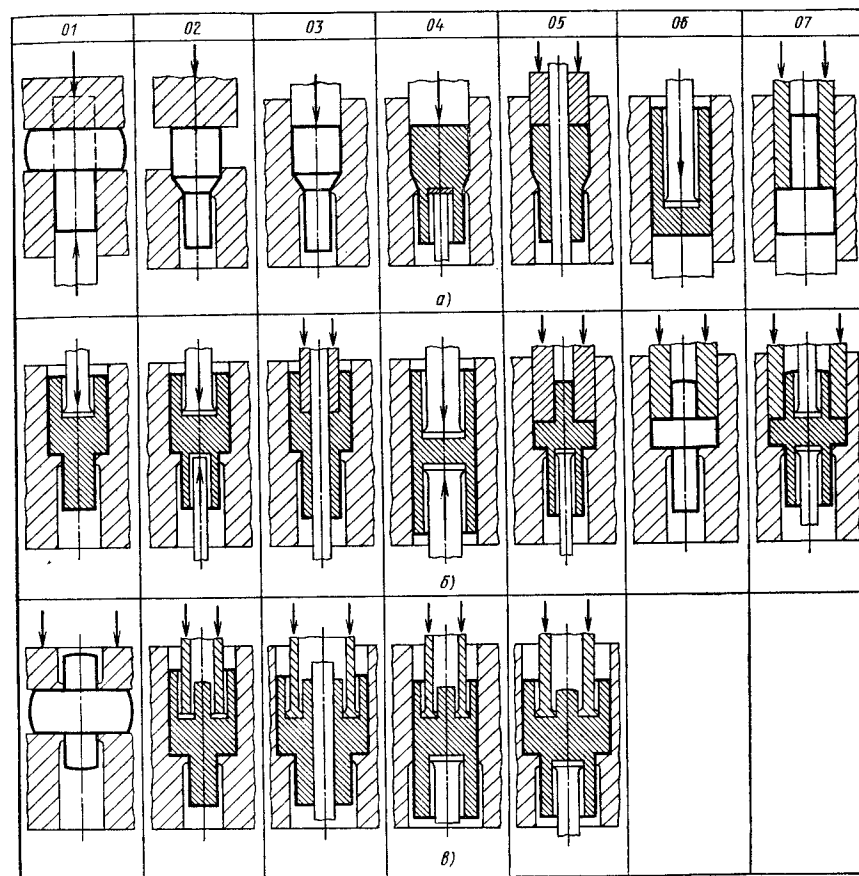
Классификация процессов выдавливания по числу направлений истечения: а — простые процессы; б — комбинированные процессы; в — совмещенные процессы; 01 — общая схема истечения; 02—07 — варианты используемых заготовок и инструмента
